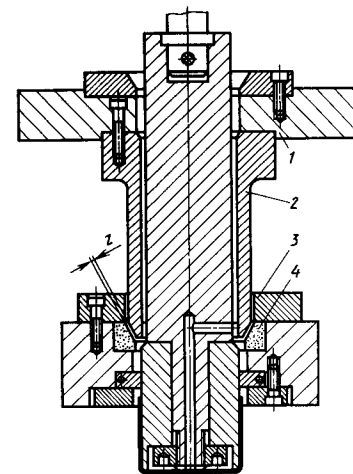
Штампы для последующей вытяжки деталей типа коробок и стаканов на прессе двойного действия
